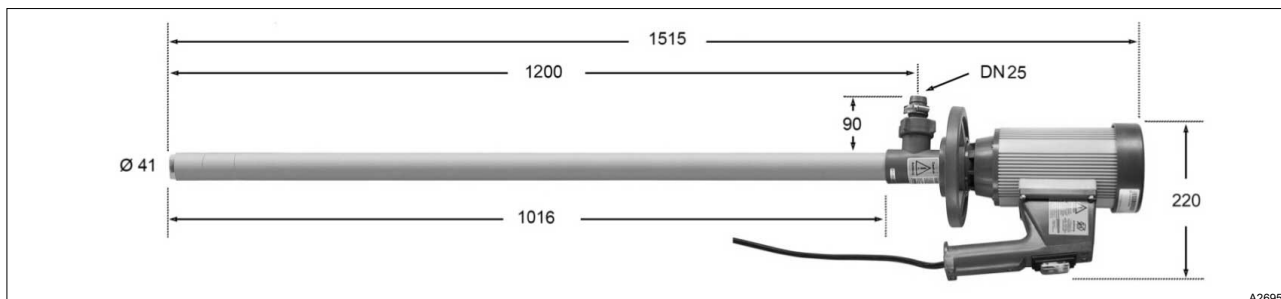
Габаритный чертеж с главными размерами, все размеры в мм.
